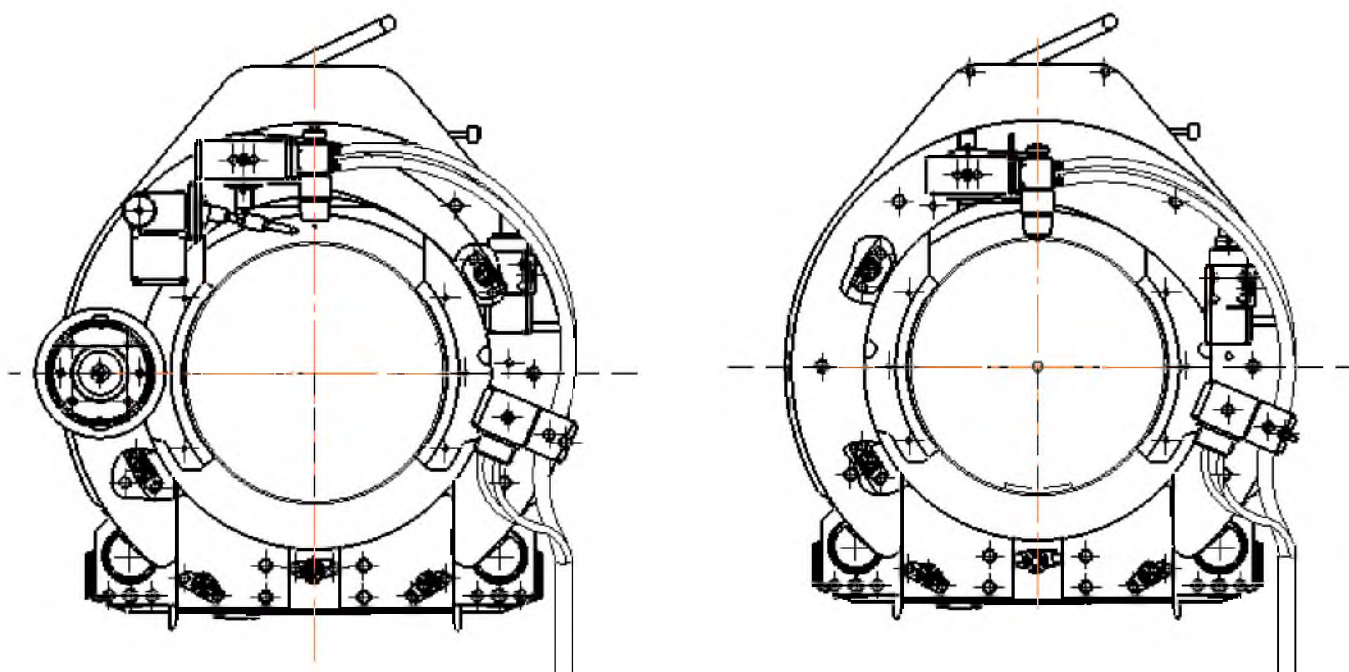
Головки для сварки трубопроводов из алюминиевых сплавов (а) и нержавеющей сталей (б)
